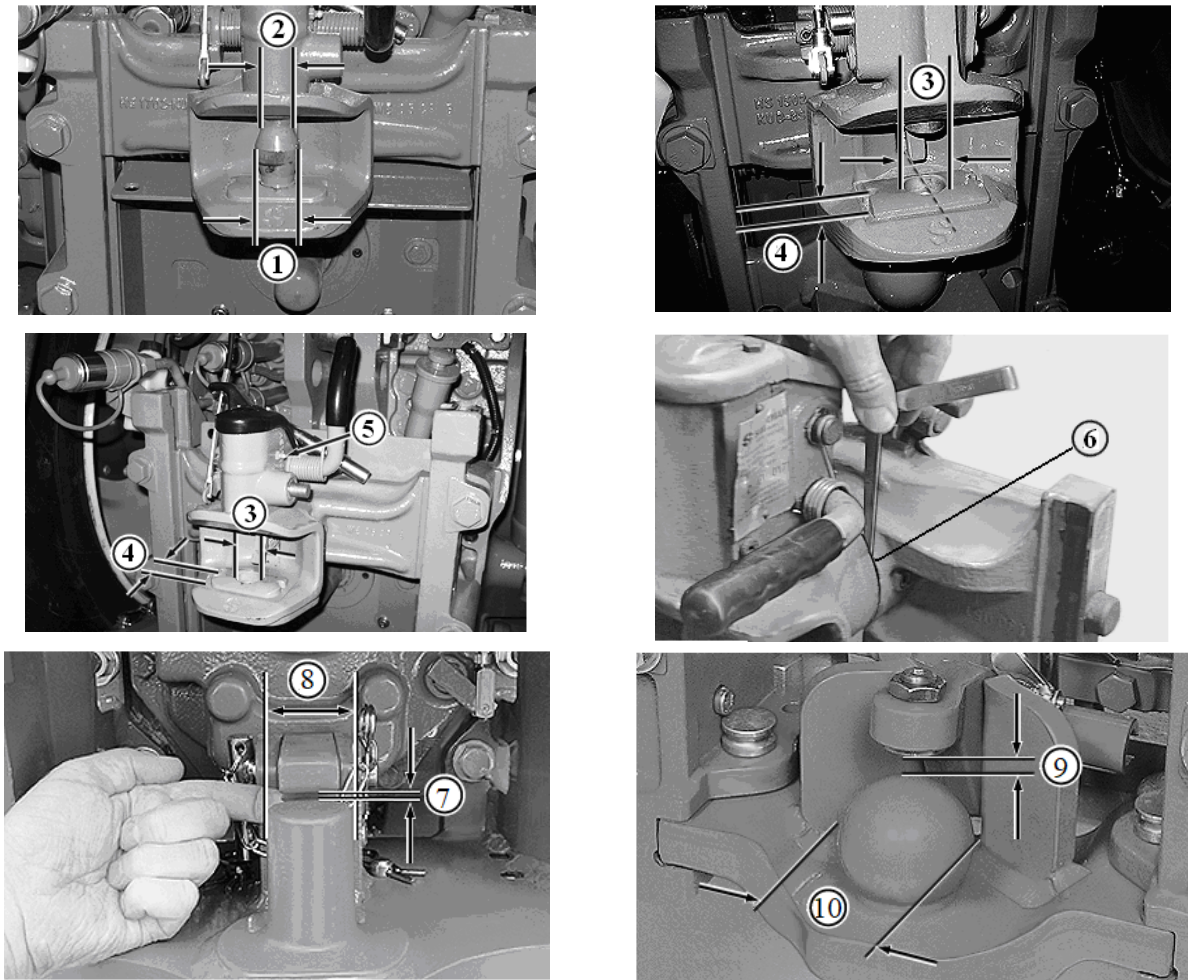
Контрольовані деталі автоматичної зчпки
